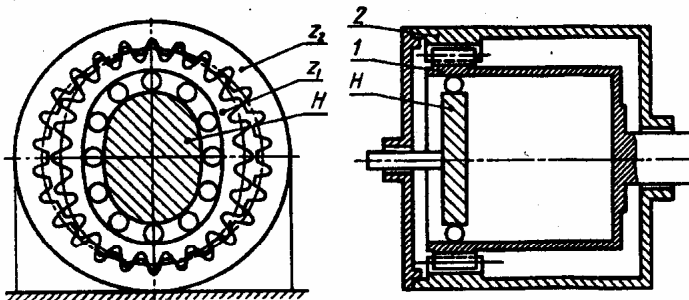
Кинематическая схема волнового зубчатого редуктора
